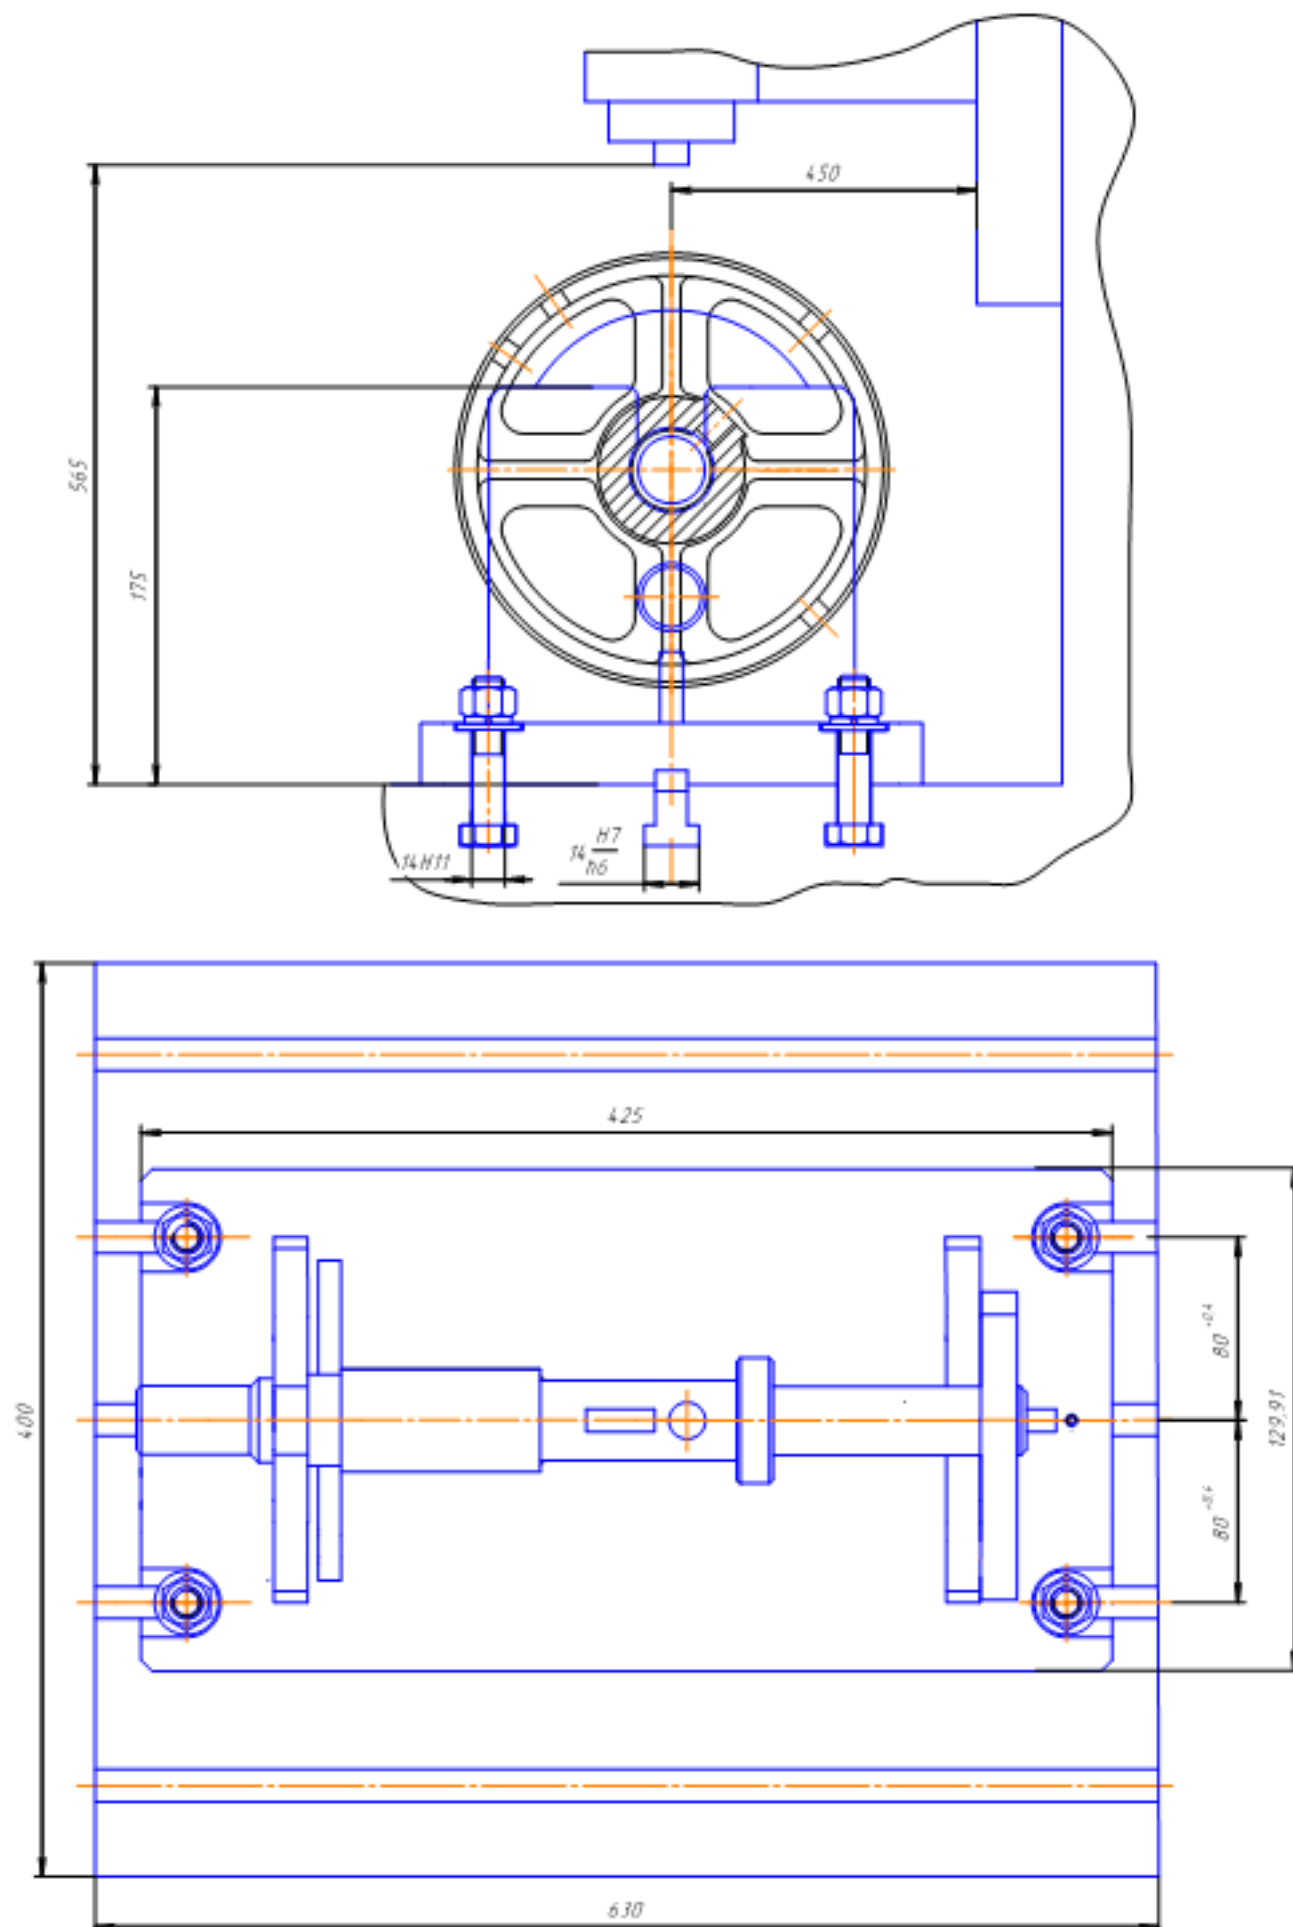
Конструкція корпусу верстаного пристосування та схема монтажу пристосування на верстаті
